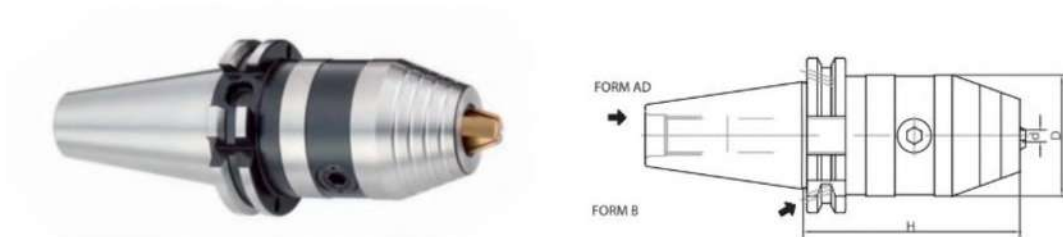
Свердлильні патрони Kintek по DIN 69871
